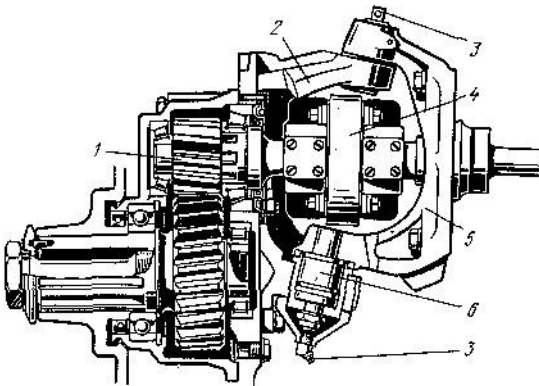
Для увеличения дорожного просвета под обеими осями фирма «Даймлер-Бенц» на автомобиле «Унимог» располагает балку оси и дышло выше оси колес, в связи с чем устанавливаются колесные редукторы. Здесь показан редуктор переднего колеса со двоярным шарниром 4 и шкворнем 6. Из-за сильной загрязняемости этой зоны необходимы две пресс-масленки 3. Остальные позиции обозначают:
